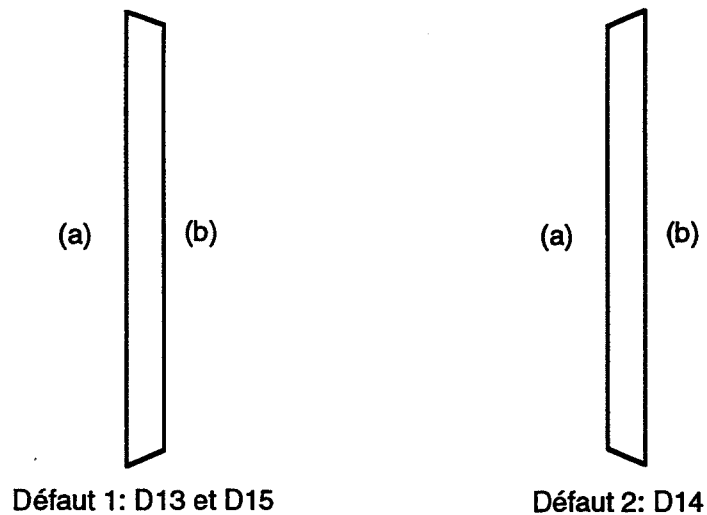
Deux types de défauts constatés sur les éprouvettes losipescu.
